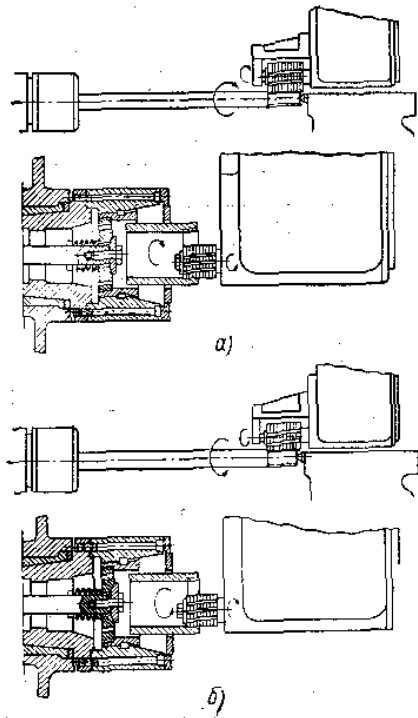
Направление вращения фрезерного шпинделя и шпинделя изделия:
